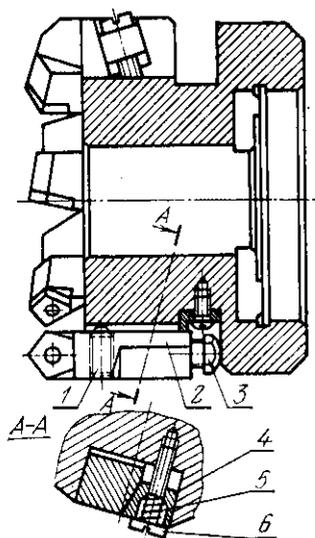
Торцевая фреза, настраиваемая на размер вне станка
